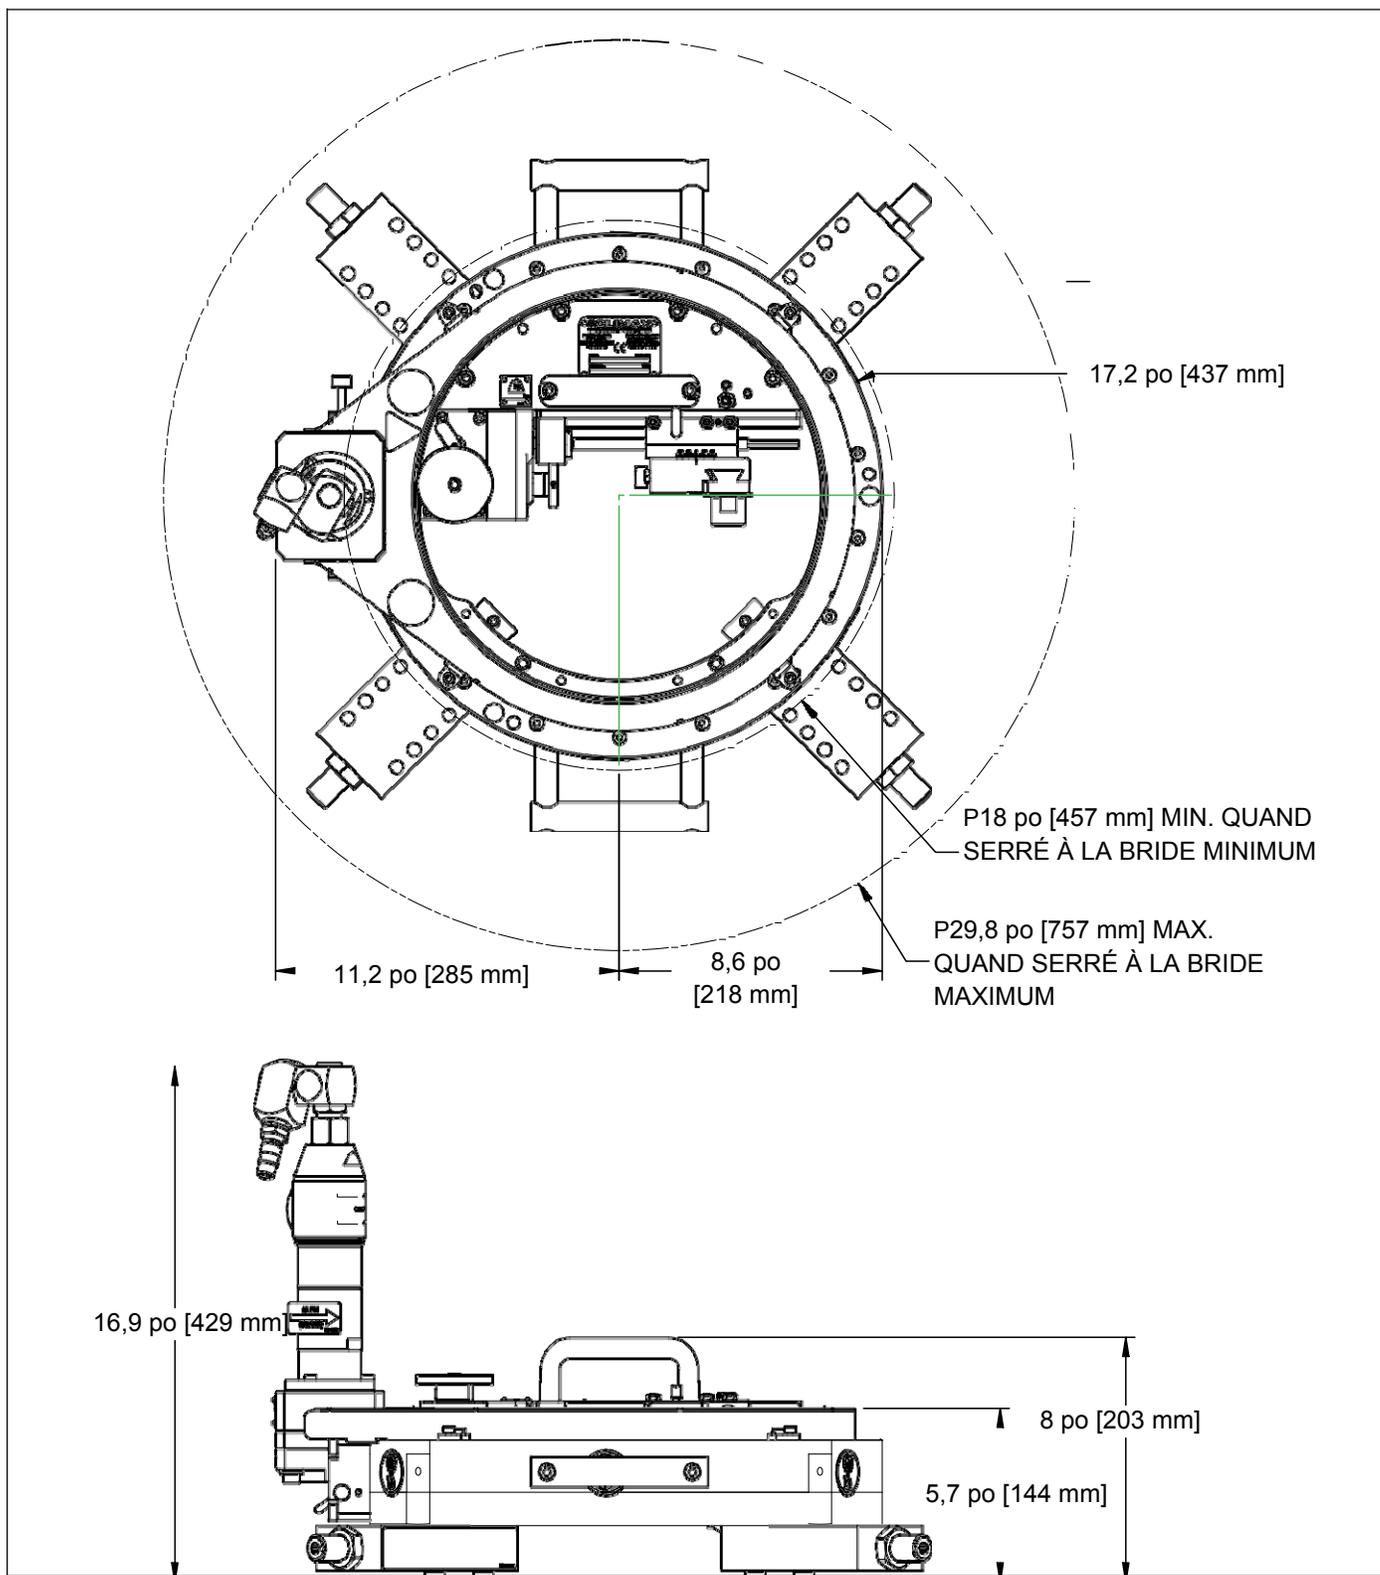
DIMENSIONS DE LA MACHINE FF1200
